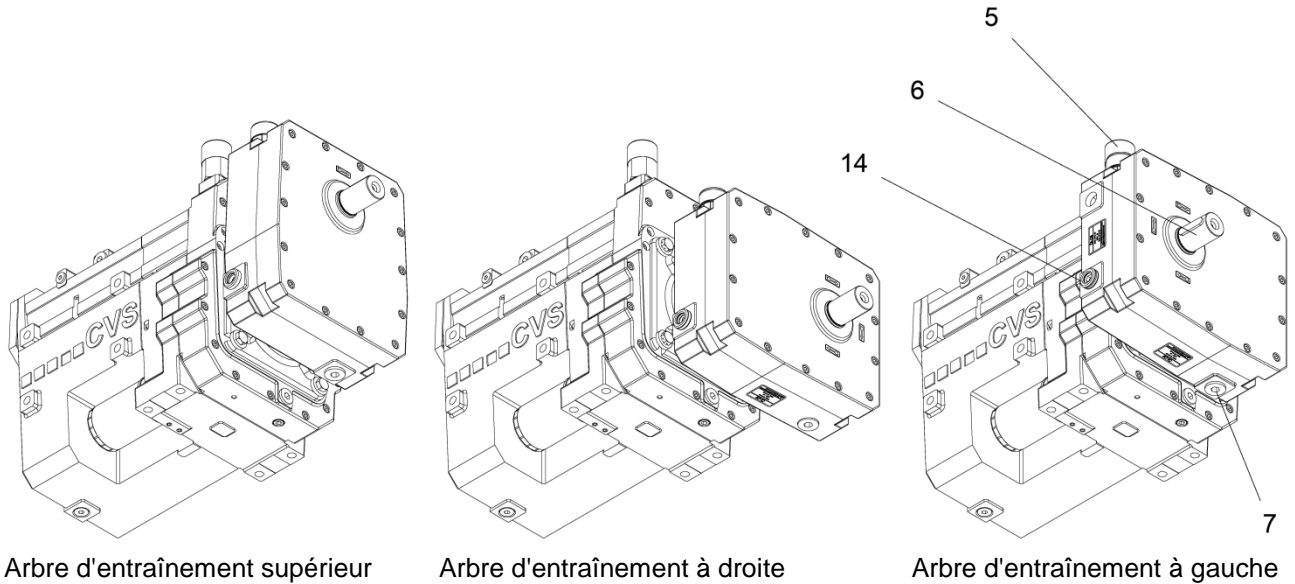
Variantes de montage pour réducteurs à engrenages, par ex. type LS
